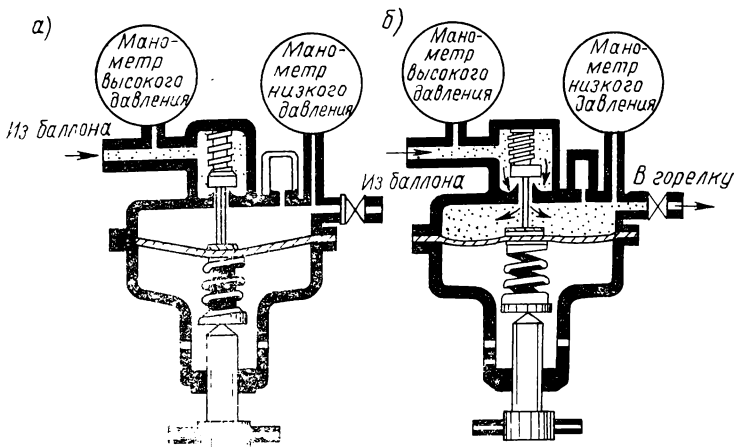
Схема работы редуктора для сжатых газов: а — газ не идет через редуктор; б — рабочее положение редуктора — газ идет в резак.
